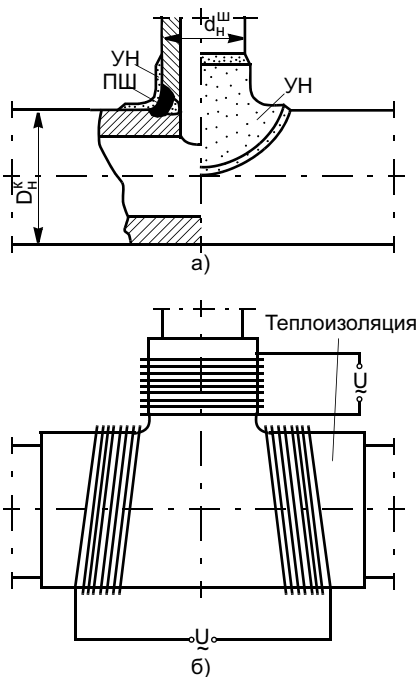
Рекомендуемая схема сварочной технологии ремонта сварного тройника  $\varnothing 245 \times 45 / \varnothing 159 \times 30$  мм (сталь 15X1M1Ф, металл шва 09X1M1Ф): а — расположение подварочного шва (ПШ) и усиливающей наплавки воротникового типа (УН); б — размещение нагревательных устройств при проведении высокого отпуска
